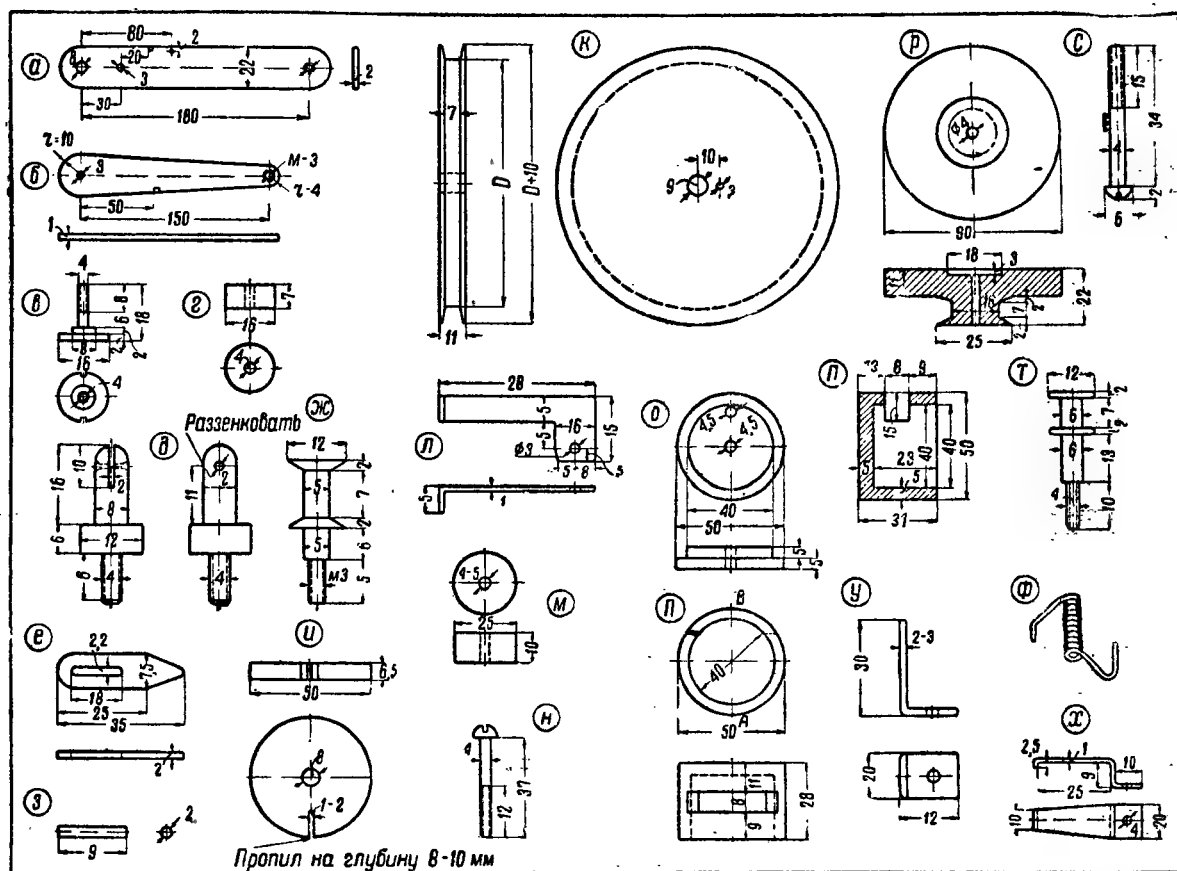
Детали любительского магнитофона. Детали а и б изготавливаются из дюралюминия или листовой стали; детали в, г, д, ж — из стали или латуни; деталь е — из стали; деталь з — из медной проволоки; деталь м (2 шт.) — из дюралюминия, стали, латуни; деталь н (3 шт.) — из стали или латуни (для крепления этой детали необходимы 4 гайки); деталь т (2 шт.) — из стали; деталь х (2 шт.) — из стали
